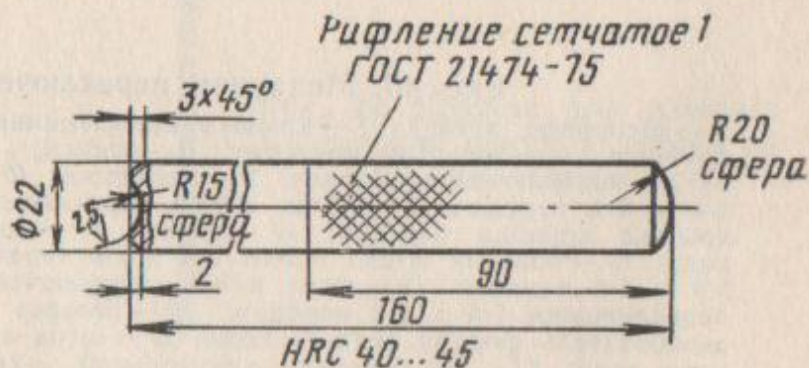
Боек для запрессовки заглушек в отверстия под пружину стопорного шарика в корпусе коробки передач
